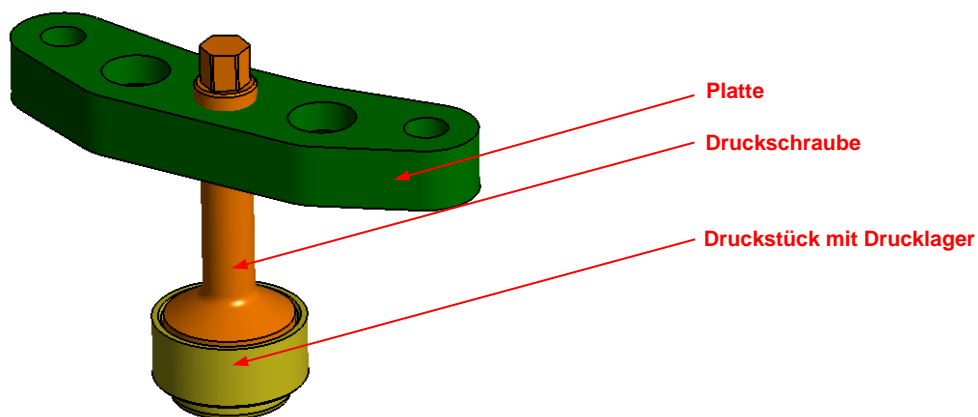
Vormontage der Platte, der Druckschraube und des Druckstücks
